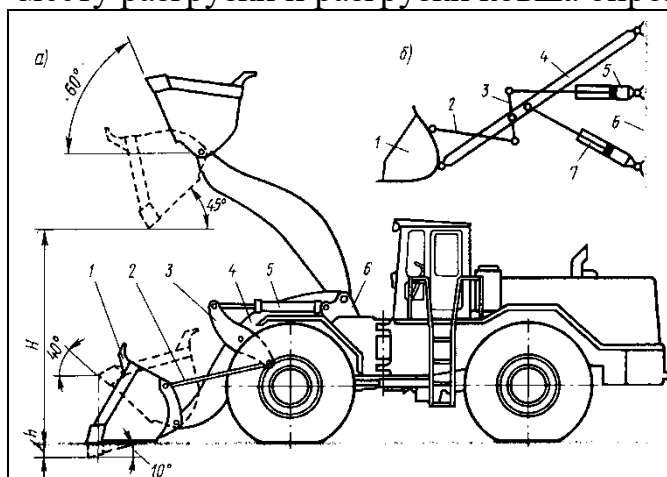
Одноковшовый фронтальный погрузчик: а—схема конструкции; б—кинематическая схема погрузочного оборудования
